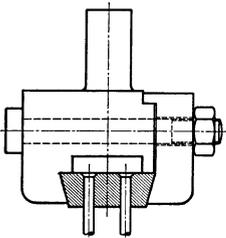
Befestigung eines Stempelfußes durch Schräge u. Zugschraube.
